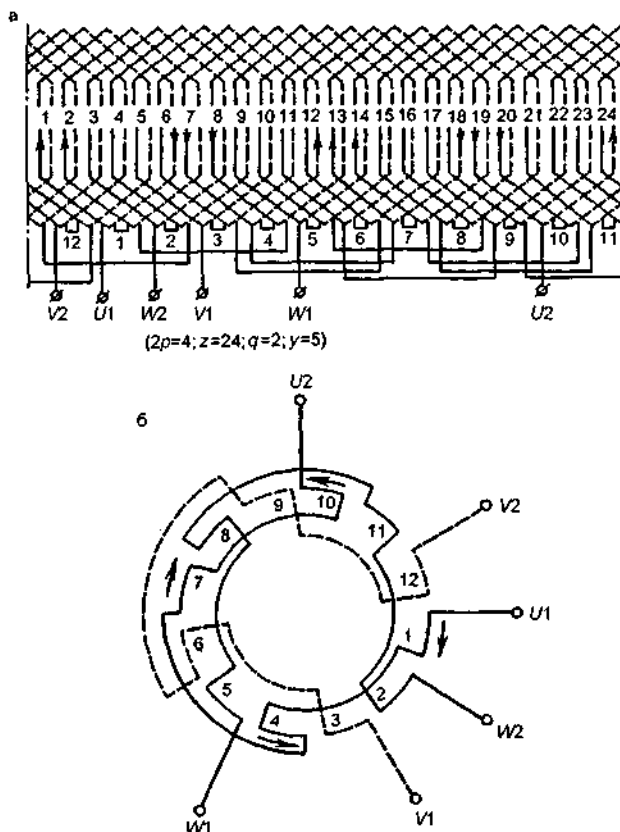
Схемы двухслойной трехфазной обмотки:
